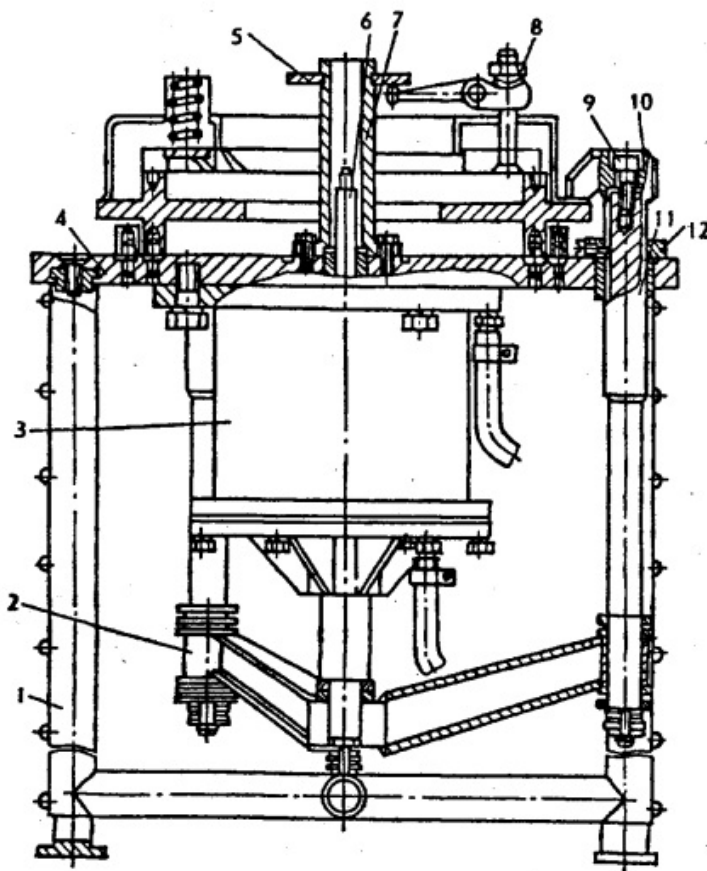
Универсальный стенд для разборки, сборки и регулировки сцепления:
